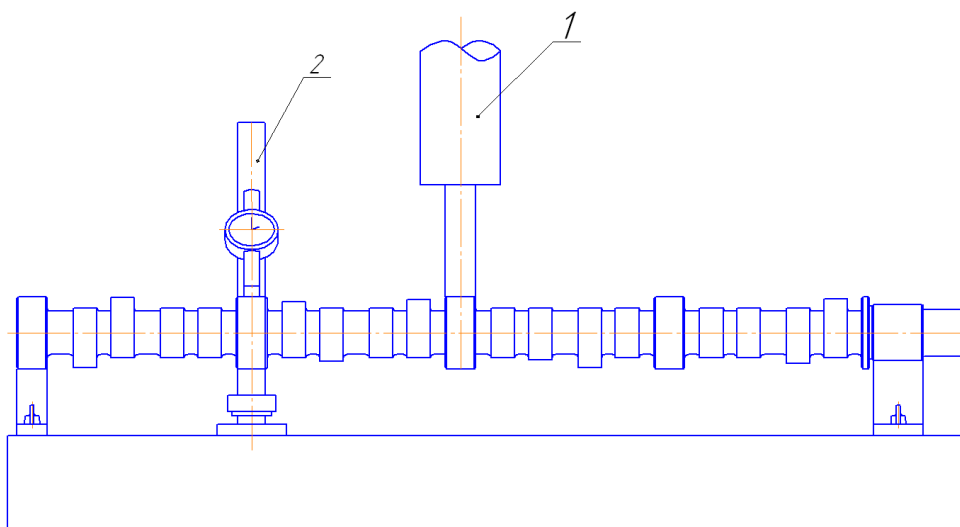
Контрольно-измерительный прибор (вид сбоку): 1 – распределительный вал; 2 – призмы опорные; 3 – часовой индикатор
